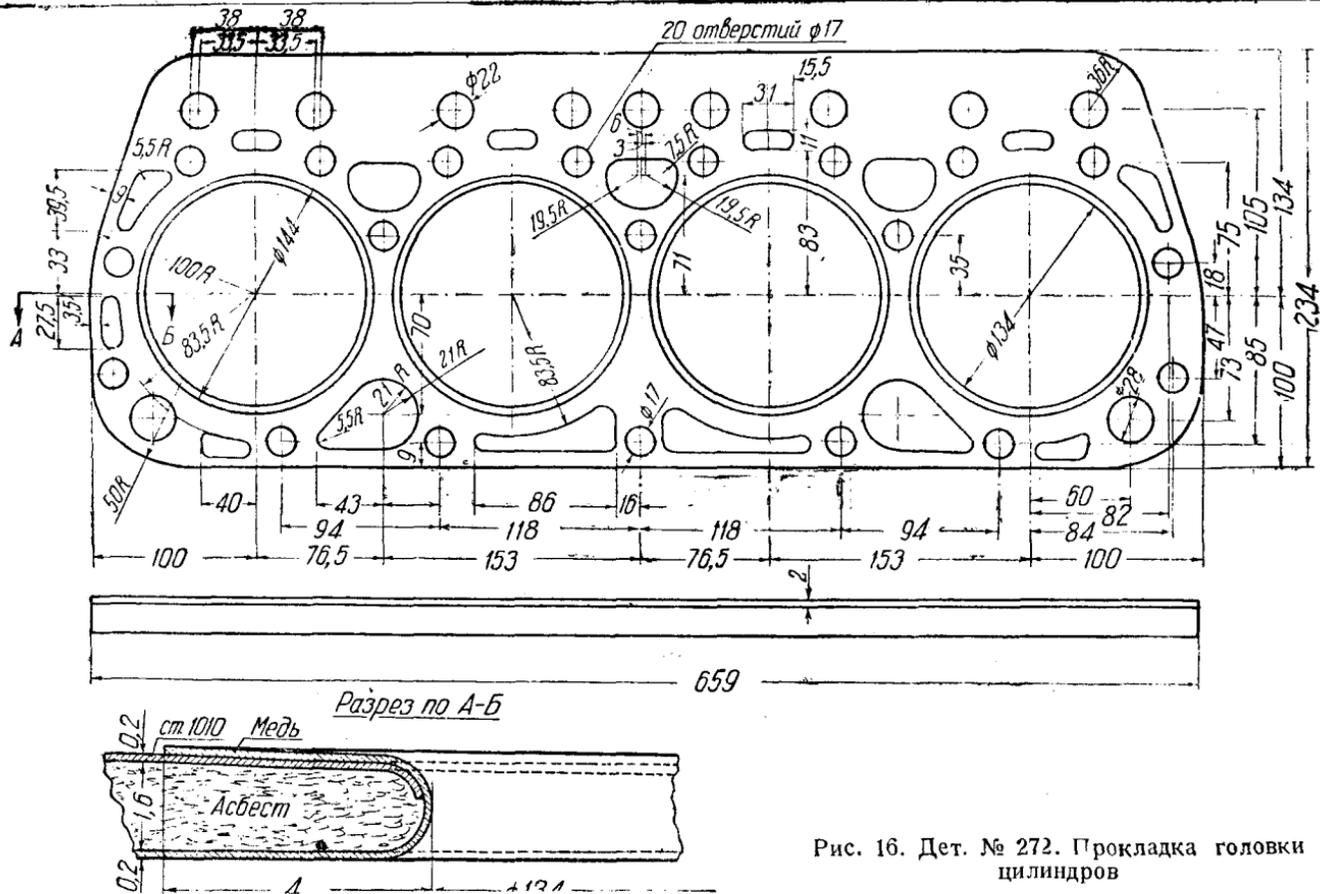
Дет. № 272. Прокладка головки цилиндров
